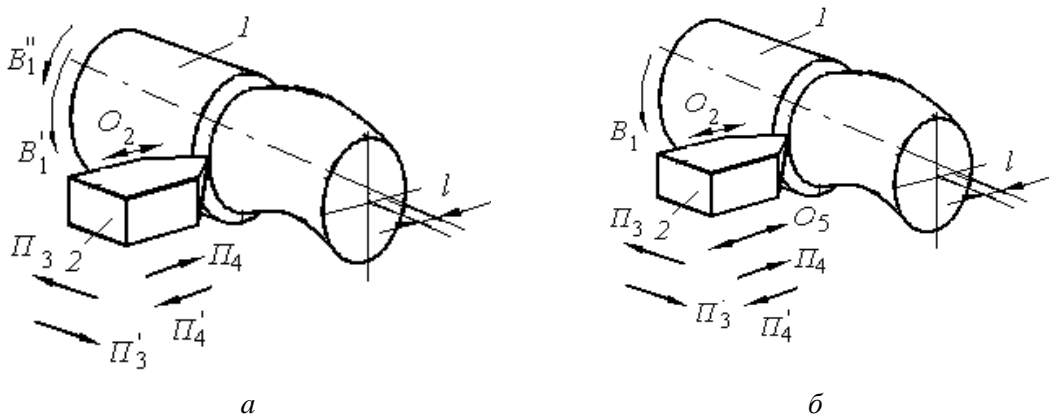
Схемы точения круговой винтовой поверхности при сообщении дополнительного движения заготовке (а) или резцу (б)
